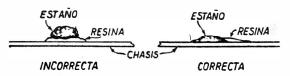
Forma en que debe hacerse la soldadura al chasis y cómo debe quedar.
